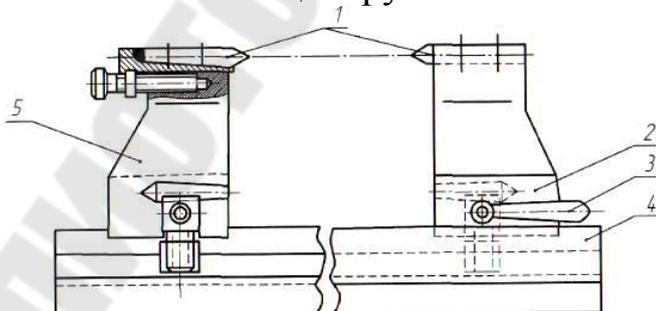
Приспособление для шлифования в центрах: 1 – центры; 2, 5 – стойки; 3 – рукоятки; 4 – плита
